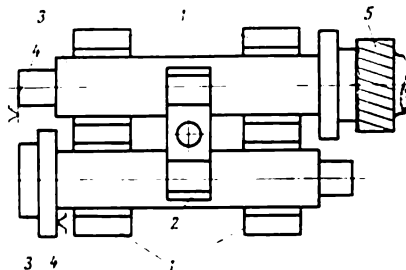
Schéma du fraisage des faces de deux ébauches sur une fraiseuse horizontale:
